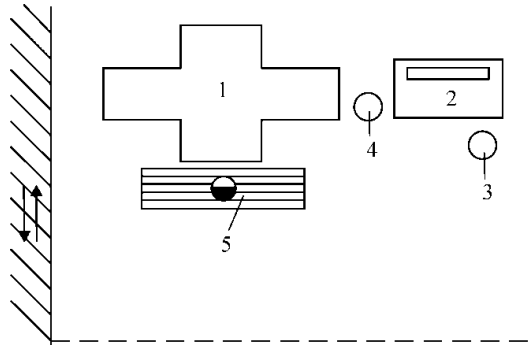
Робоче місце коваля-штампувальника (площа 8,3 м²): 1 – прес агрегатний; 2 – тумбочка для інструменту; 3 – стілець підйомно-поворотний; 4 – урна для сміття; 5 – решітка для ніг.
